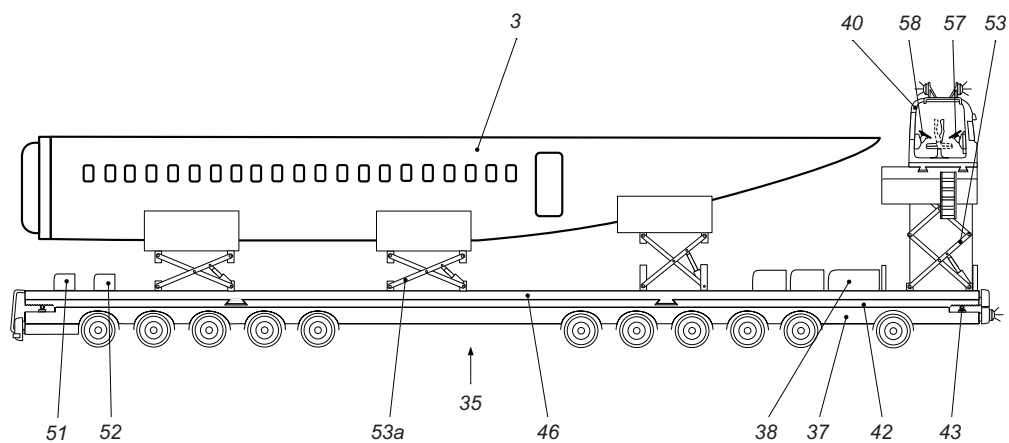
Транспортний засіб зі знятими бортами, із закріпленої на ньому нижньої частини фюзеляжу в положенні для стикування з верхньою частиною фюзеляжу
